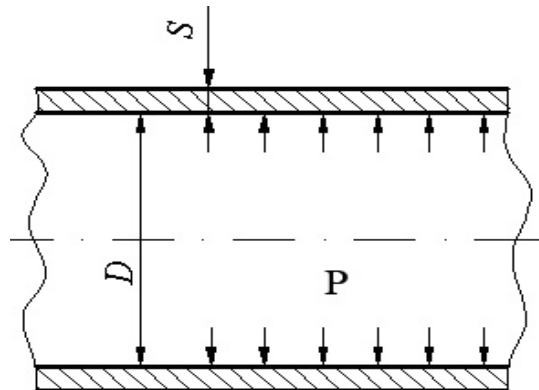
Розрахункова схема циліндричної обичайки
